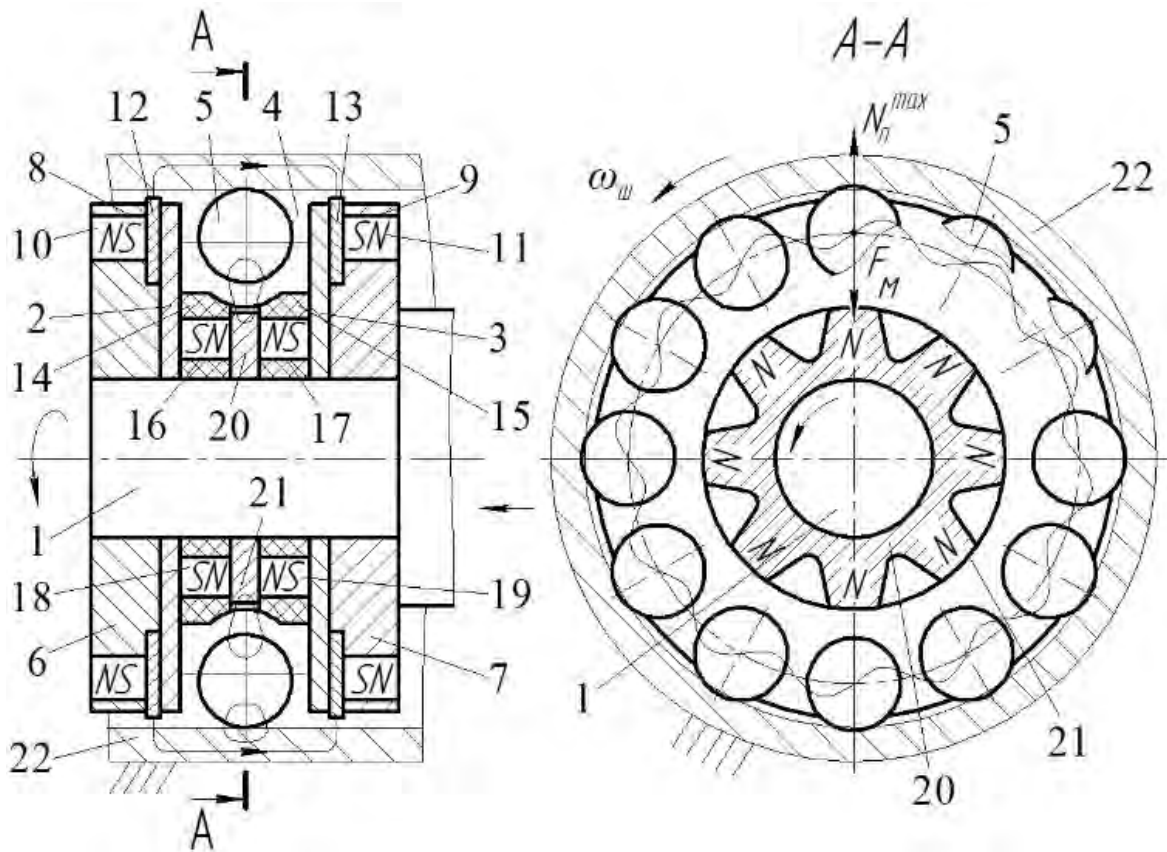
Комбинированный инструмент для совмещенной магнитно-динамической обработки: 1 – оправка; 2, 3 – шайбы; 4 – кольцевая камера; 5 – ферромагнитные деформирующие шары; 6, 7 – диски; 8, 9 – аксиальные отверстия; 10, 11, 16, 17 – магнитопроводы; 14, 15 – обоймы; 20 – магнитопроводный диск; 21 – периодическая поверхность; 22 – ферромагнитный цилиндр
